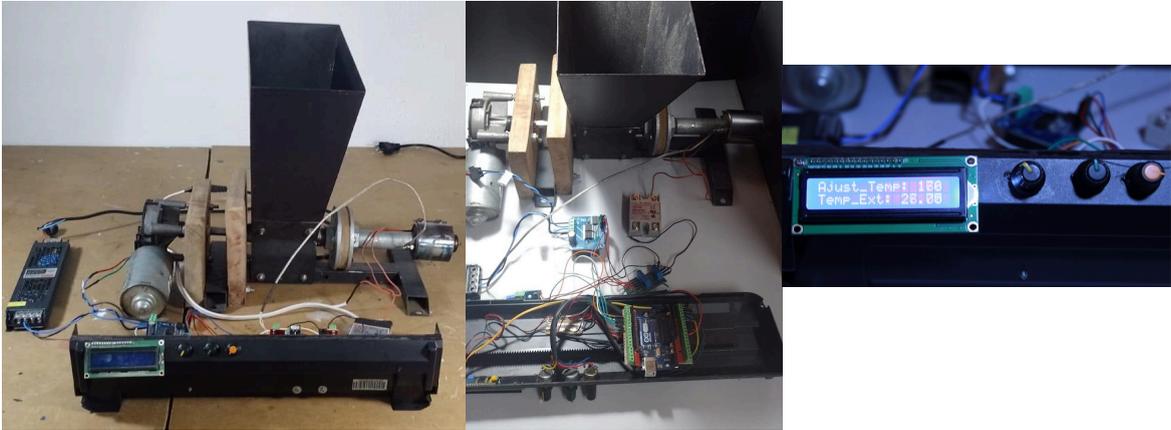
Extrusora montada (esq.); Circuito elétrico da extrusora(centro); Painel de controle (dir.).
